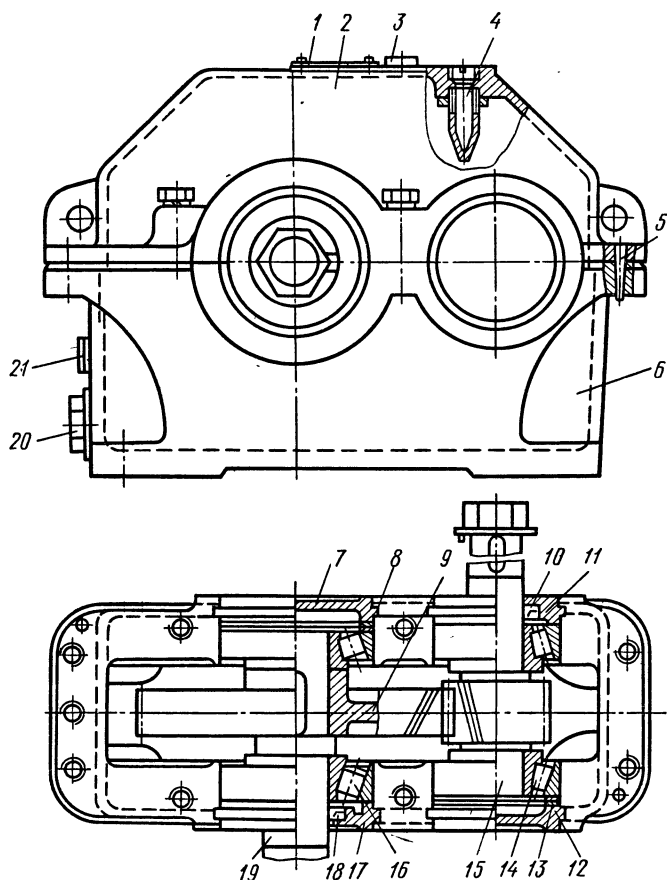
Редуктор цилиндрический одноступенчатый с косозубыми колесами
